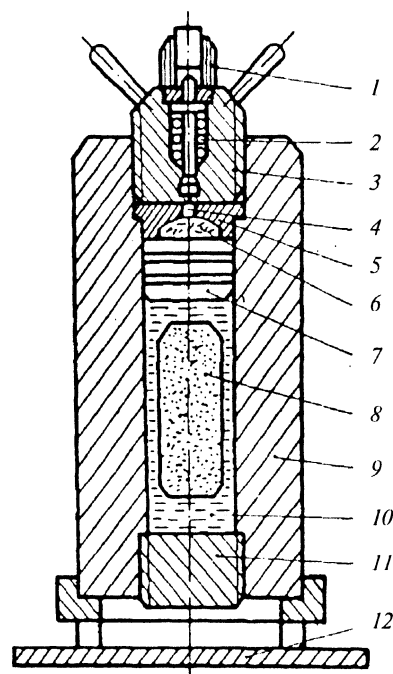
Схема гидродинамической машины: 1 – ударный механизм; 2 – пружина; 3 – верхняя крышка; 4 – капсюль-воспламенитель; 5 – гильза; 6 – заряд пороха; 7 – поршень; 8 – прессуемая заготовка; 9 – корпус; 10 – рабочая среда; 11 – нижняя крышка; 12 – опора
